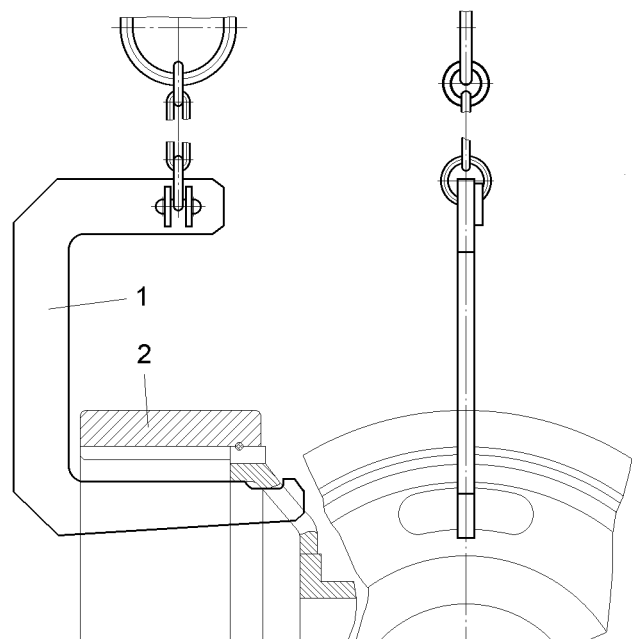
Чалка для перемещения коронной шестерни с кожухом колесной передачи:
